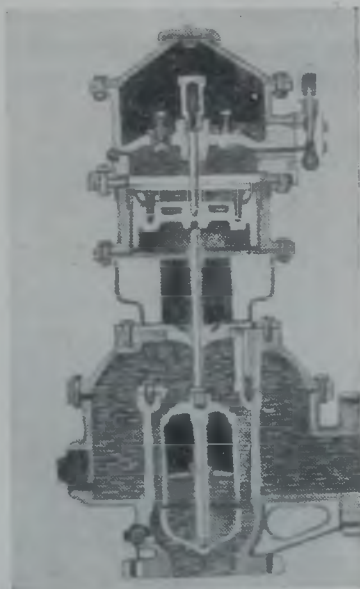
Клапан для выпуска воздуха (по материалам Simplex Valve and Meter Co.)
